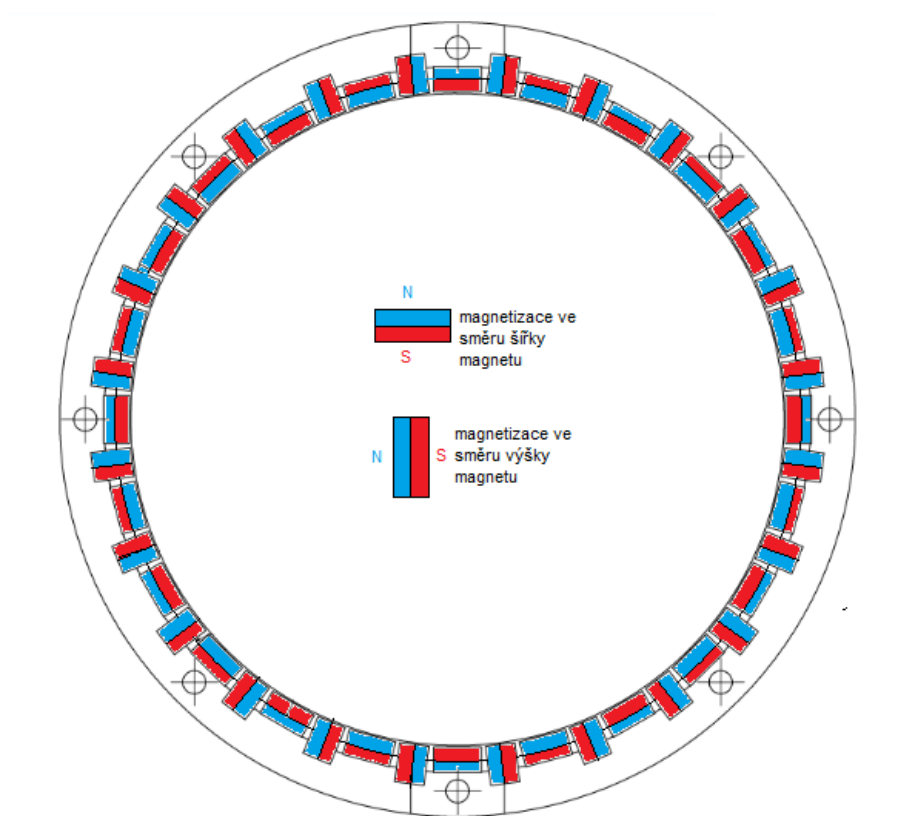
Klasický rotor funkčního vzorku BLDC stroje
